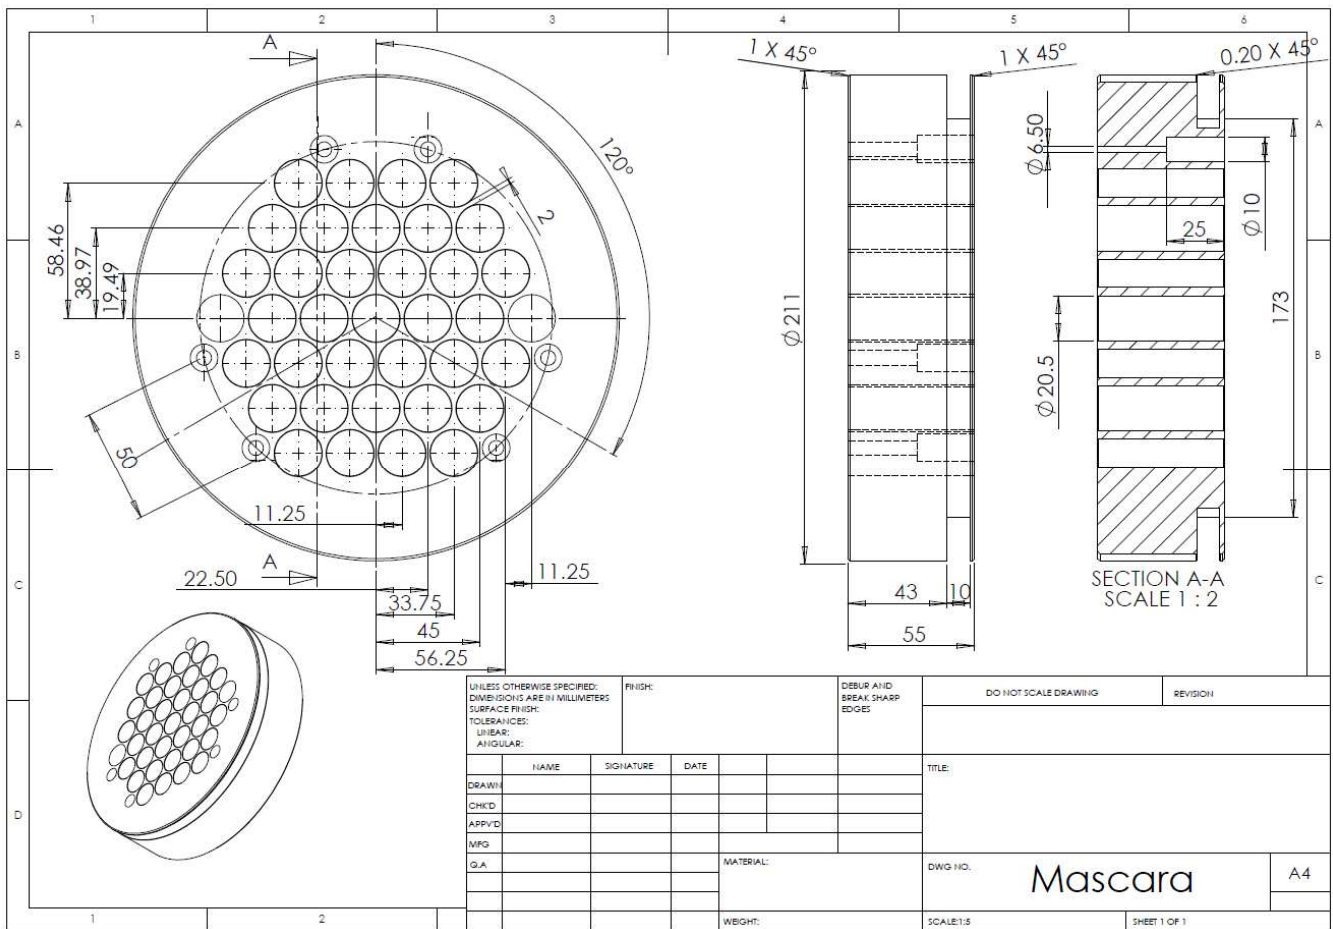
Desenho técnico para o suporte das bobinas excitadoras do sistema BAC Planar 3.
